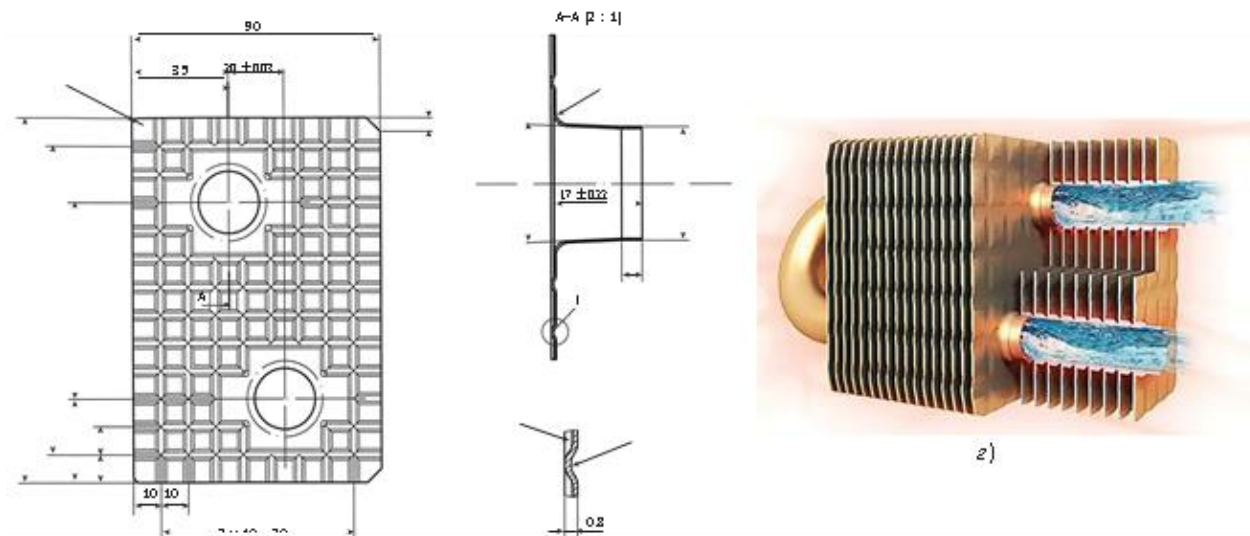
Схема двухтрубного элемента КП 20, типоразмер 1 (а–в) и сборка из двухтрубных элементов КП-20 в разрезе (г). а – пластина с двумя трубами (верхней и нижней); б – конус, из которых набрана труба с ребрами в виде пластин с вы- ступами; в – выступ на пластине
